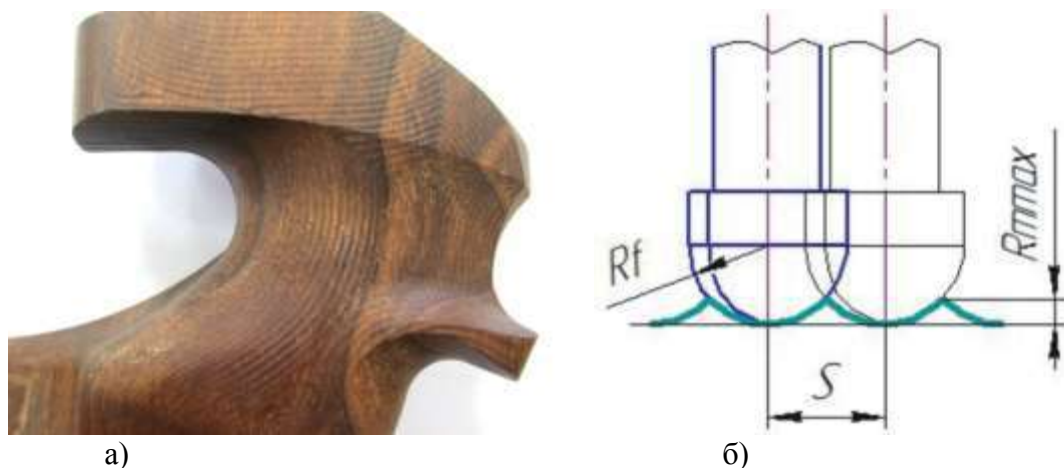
поверхность рукоятки с шагом поперечной подачи 1,3 мм (а); схематичное изображение получения фактуры при чистовой обработке шаровой фрезой (б)
